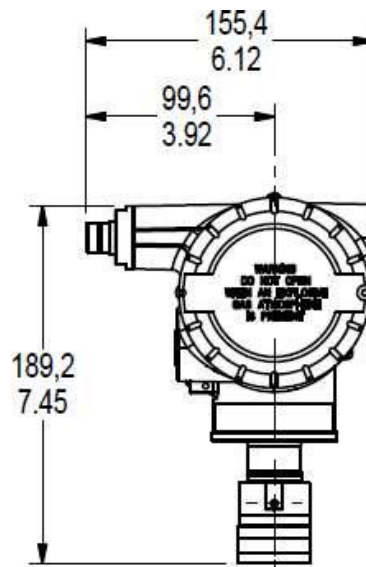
Dimensions de montage standard en ligne pour STAW74L (adaptateur distant illustré)
